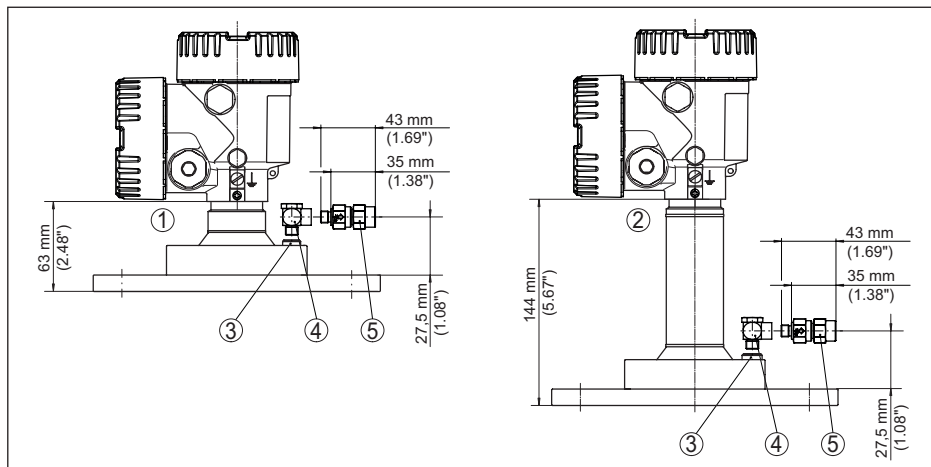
NCR-86, flange com antena lentiforme e conexão de ar de limpeza
